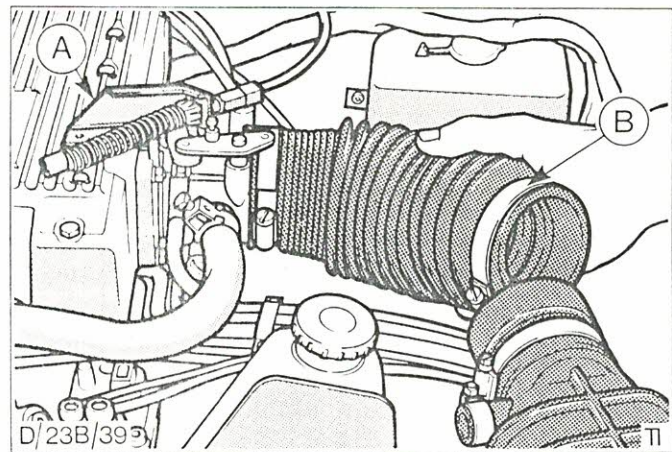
Befestigungsschrauben - Zusatzluftschieber
